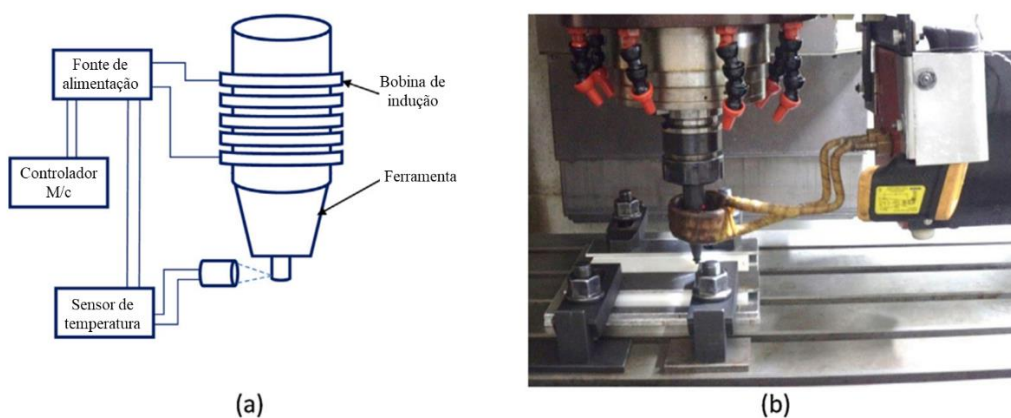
i-FSW: a) Representação esquemática, b) Montagem experimental., adaptado de [27].
